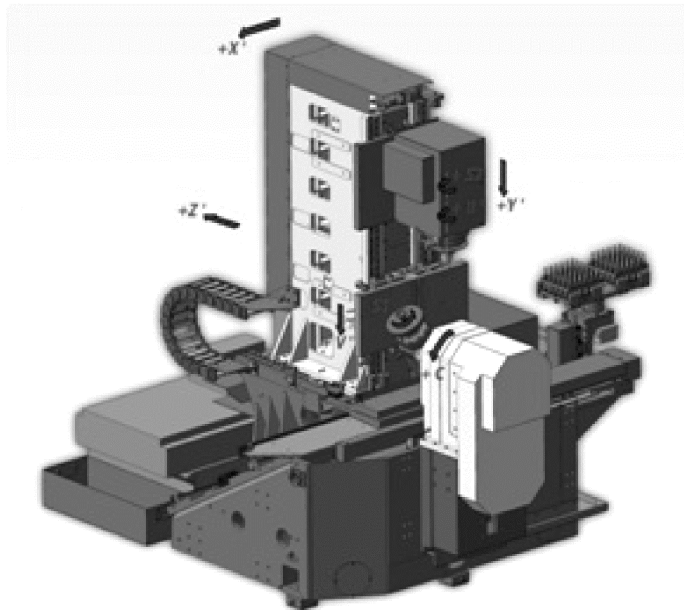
Компонировочная схема многокоординатного шлифовально-заточного станка с ЧПУ модели С-300
